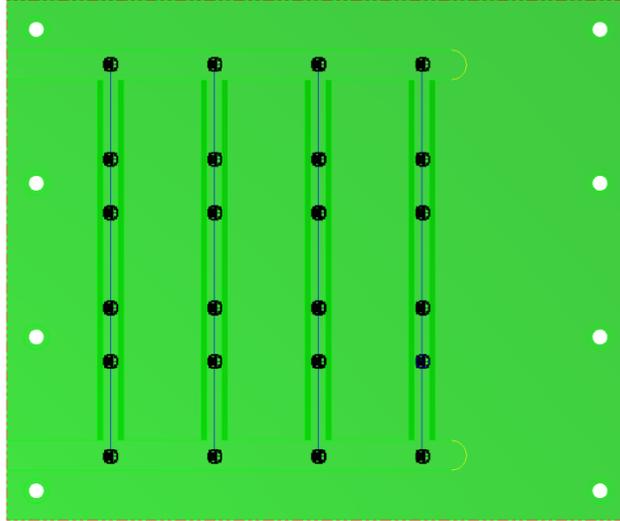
Posiciones de la herramienta durante el maquinado.
